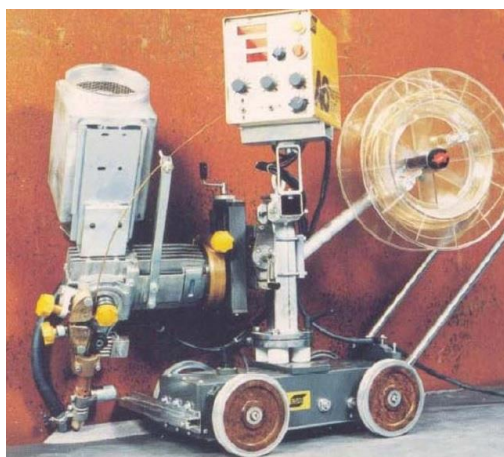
Equipamento para soldadura com o processo SAS
